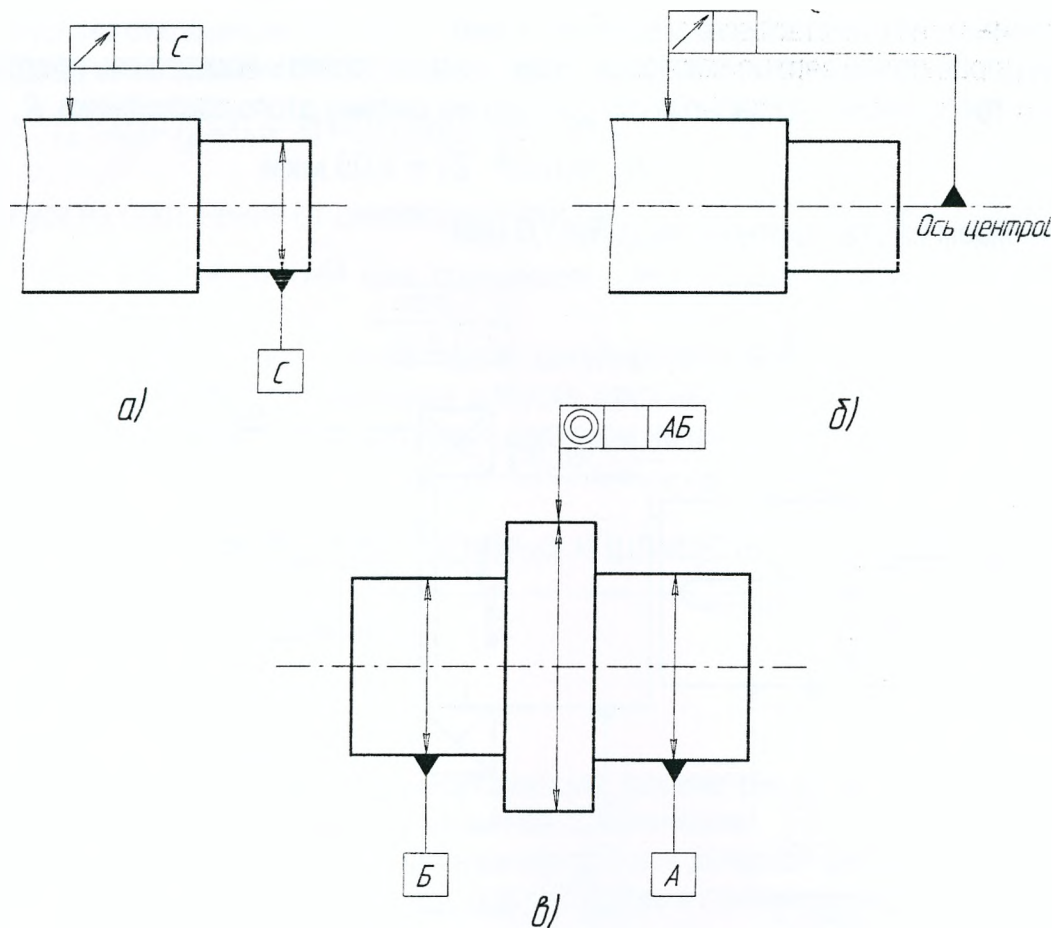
Нанесение баз и допусков расположения:
